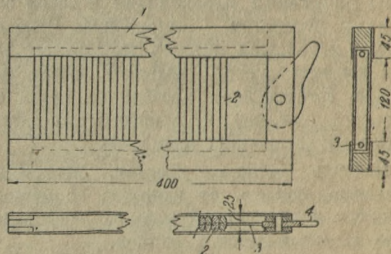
Конструкция узкой рамы на два ряда пластинок
